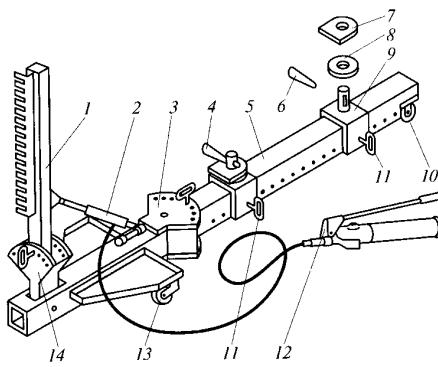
Силовое поворотное устройство БС-124.000 для правки кузовов:
